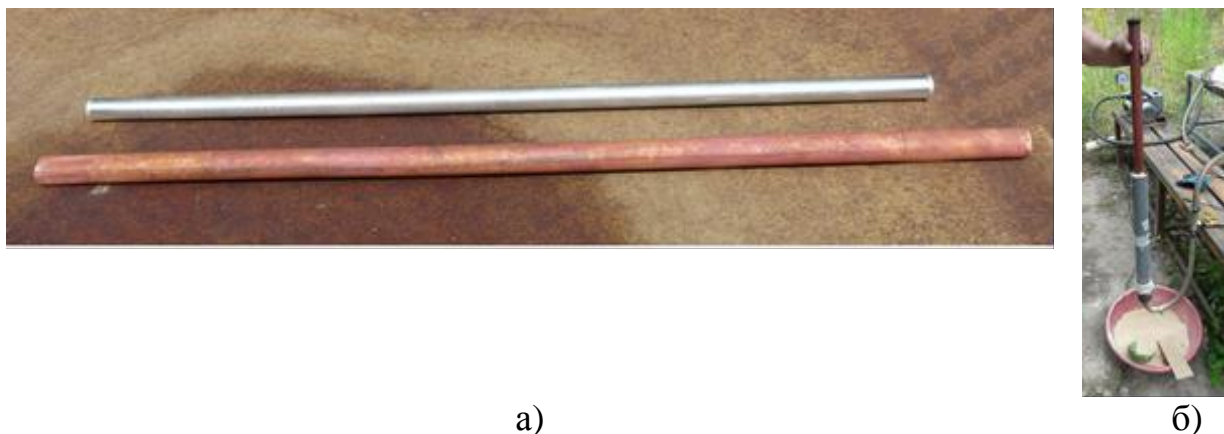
Заготовки для зварювання вибухом (а), засипка вибухової речовини у складовий контейнер (б)
